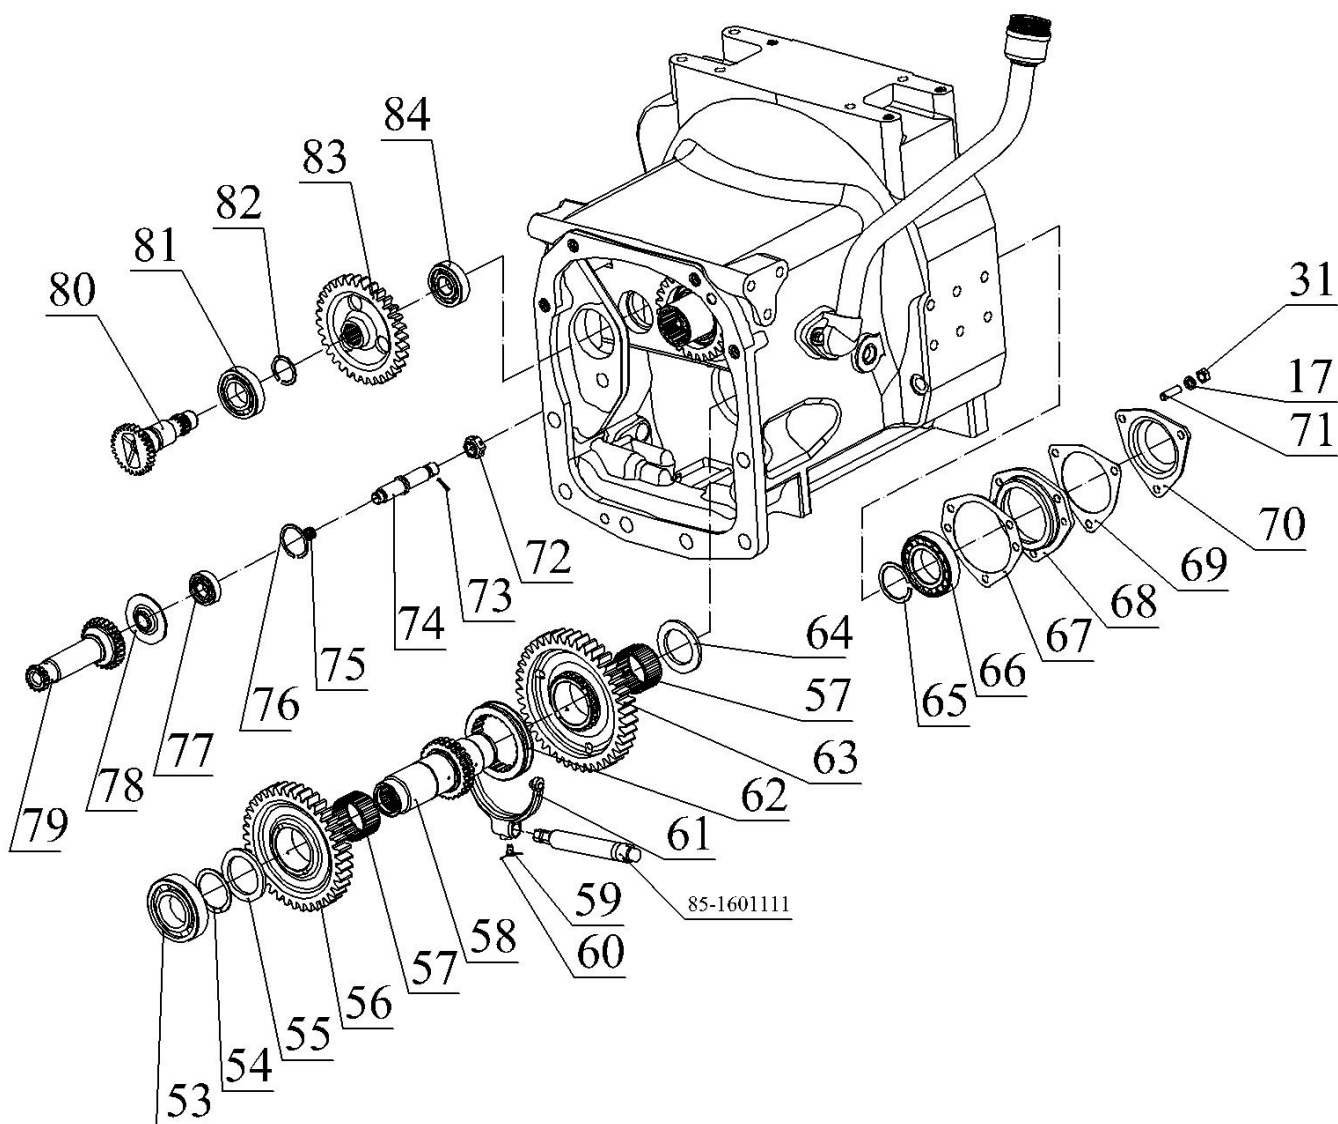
Корпус сцепления (лист 3 из 3)
